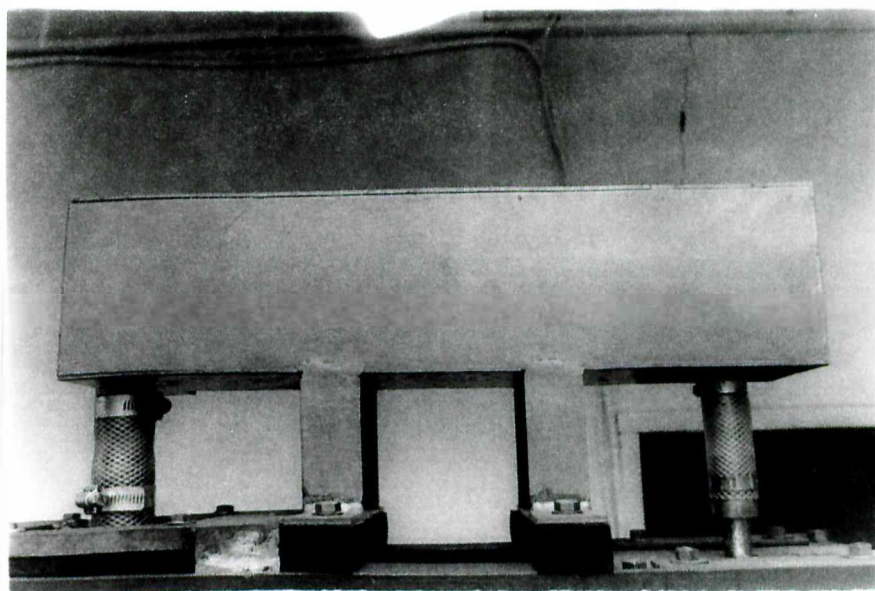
Vista do Redutor que transmite o movimento do motor para o fuso de esferas recirculantes.
